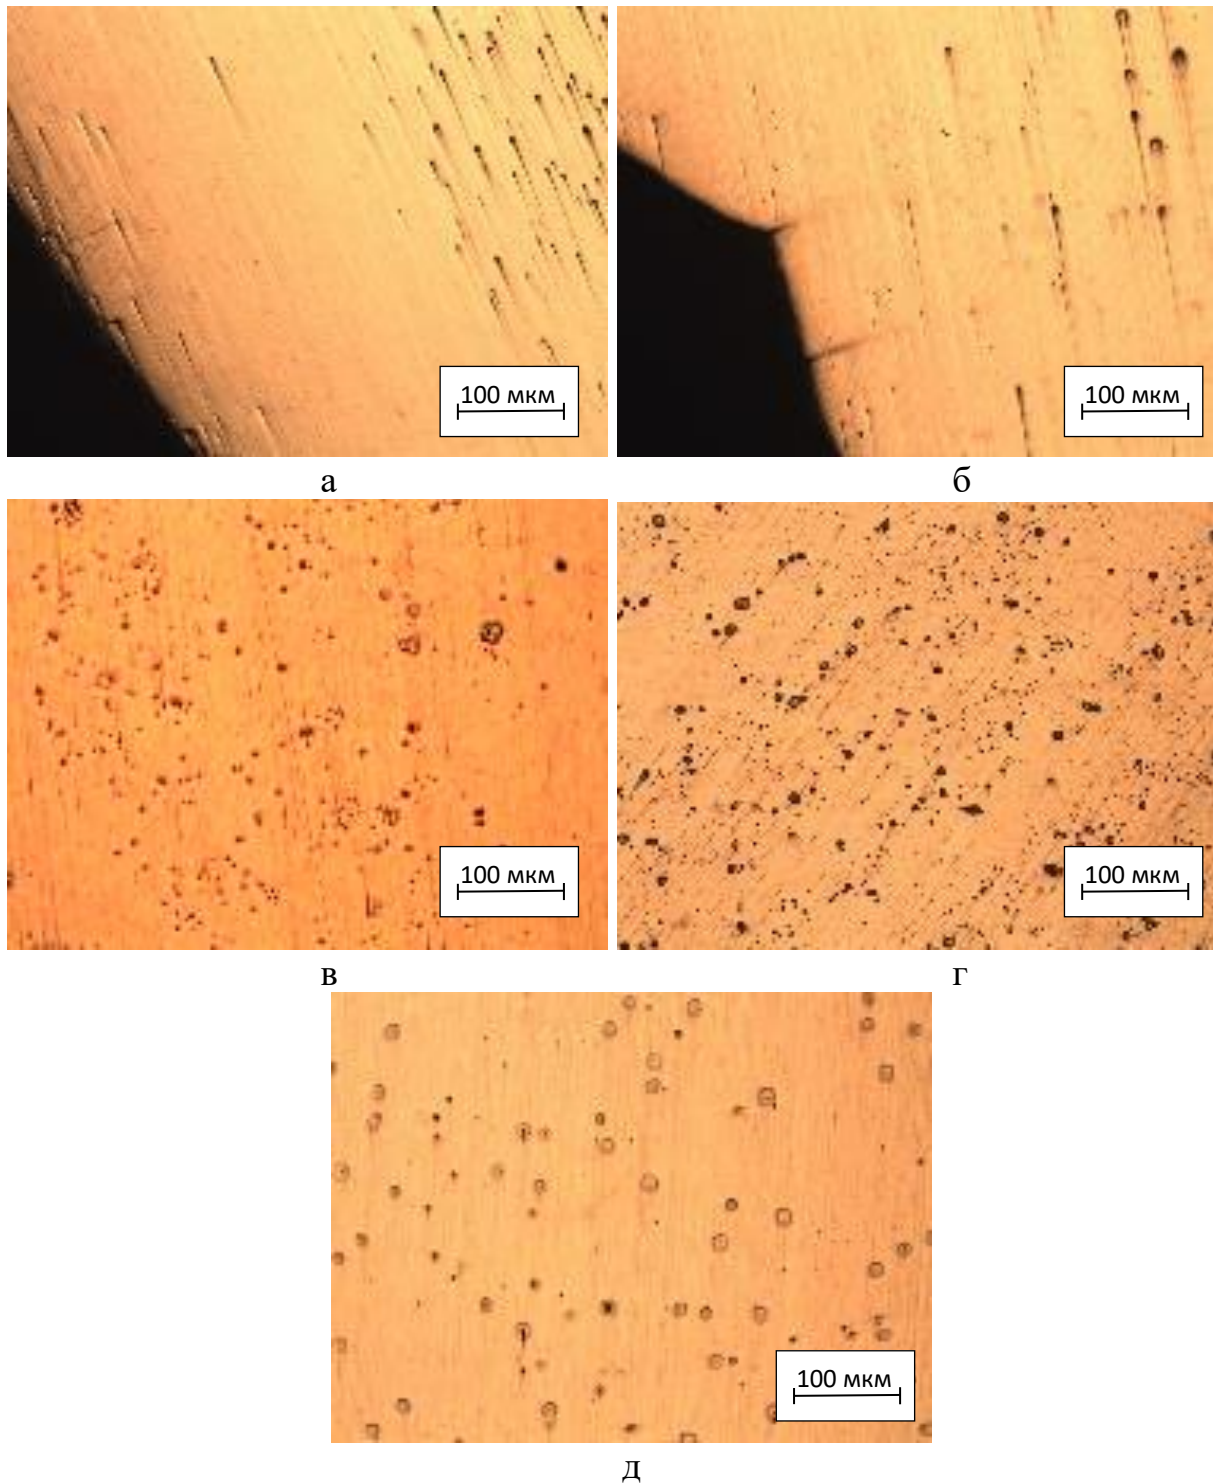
Силикатные и оксидные включения в металле сварного шва поверхностной зоны (а, б), в центральной части сварного шва (в, г) и в структуре основного металла (д) при использовании флюса АН-67 с 2 % добавкой углеродфторсодержащего материала
